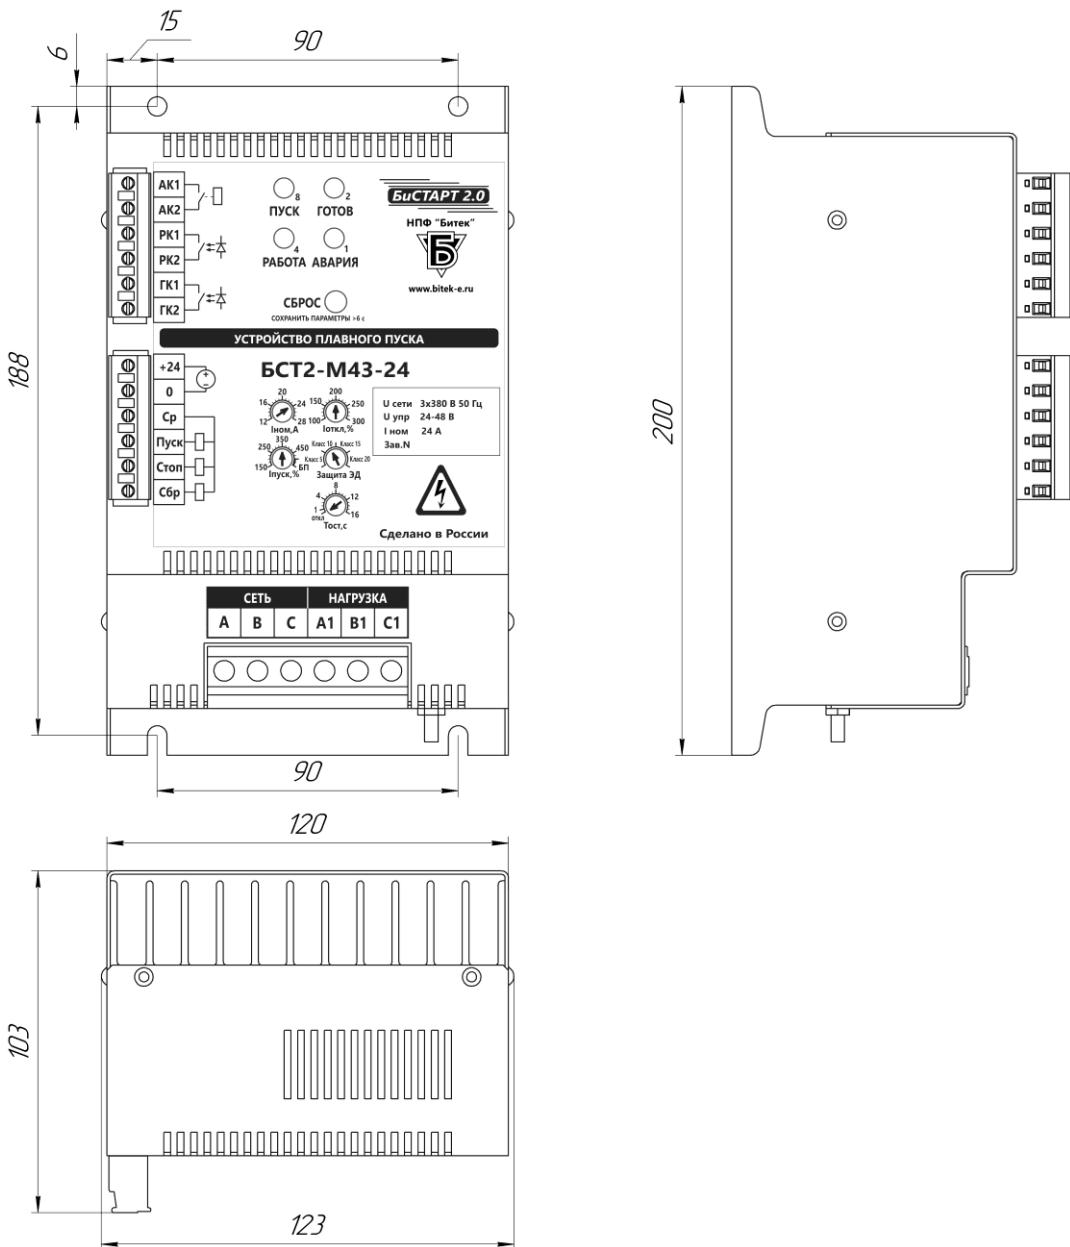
Габаритно-установочные размеры БСТ2-...-03 (-06, -12, -16, -24)
